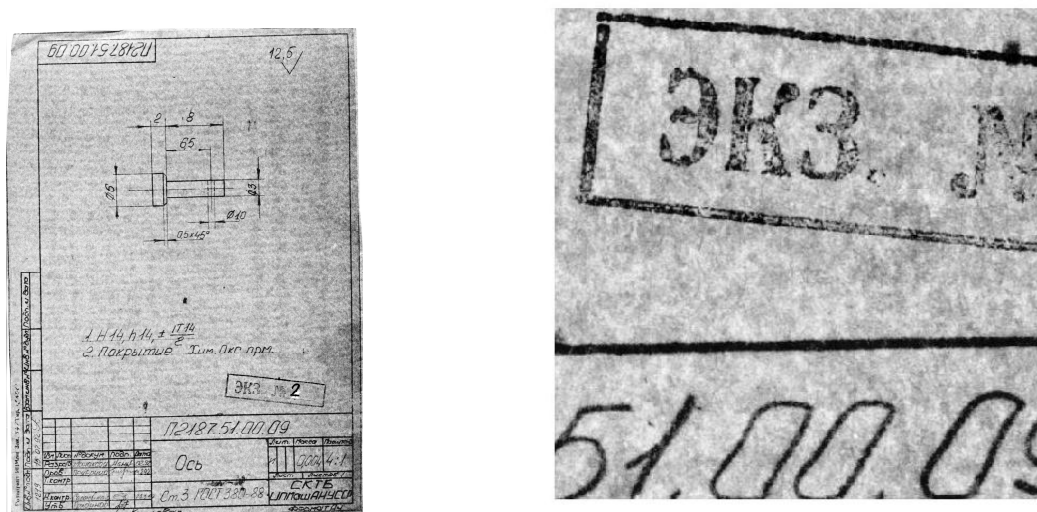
Загальний вигляд зображення конструкторського кресленника та його фрагмент
